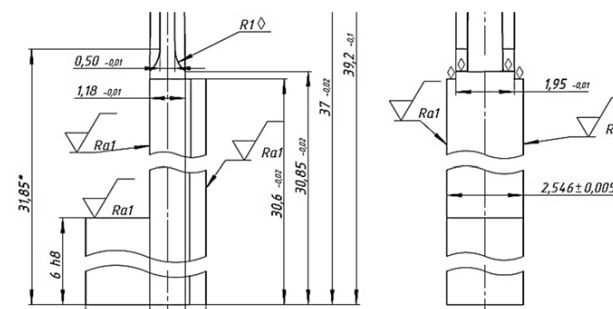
Фрагмент чертежа знака сборной формообразующей оснастки
